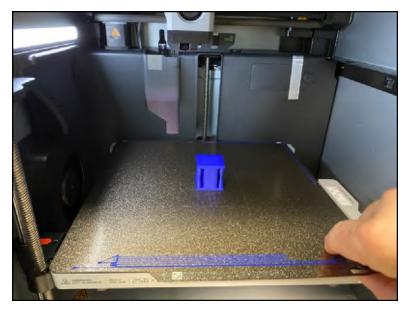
Soulever légèrement un coin du plateau magnétique pour décoller la pièce.
